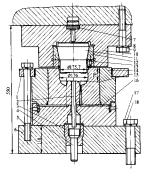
闭式模银带助银件用的模具 1—某協關 2—顶杆; 3—导筒; 4—推杆; 5.9、17—紧闭螺栓; 6—底板; 7—定位器; 8、18—整圈; 10—冲头模座; 11—冲头; 12—他形圈; 13—螺纹紧闭圈; 14—四域模签; 15—四模; 16—萤板
